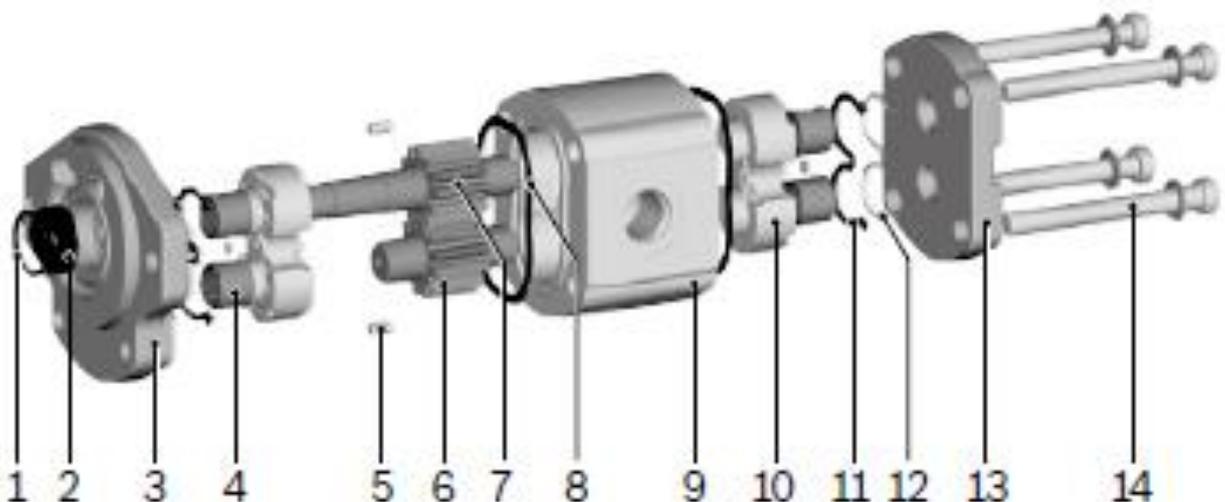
Componentes de bomba de engranajes con cuerpo de aluminio. [10]
